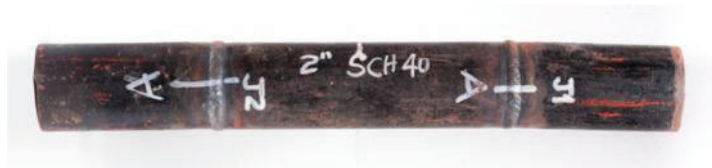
Cupón de prueba soldado 2" SCH STD- Proceso GTAW
